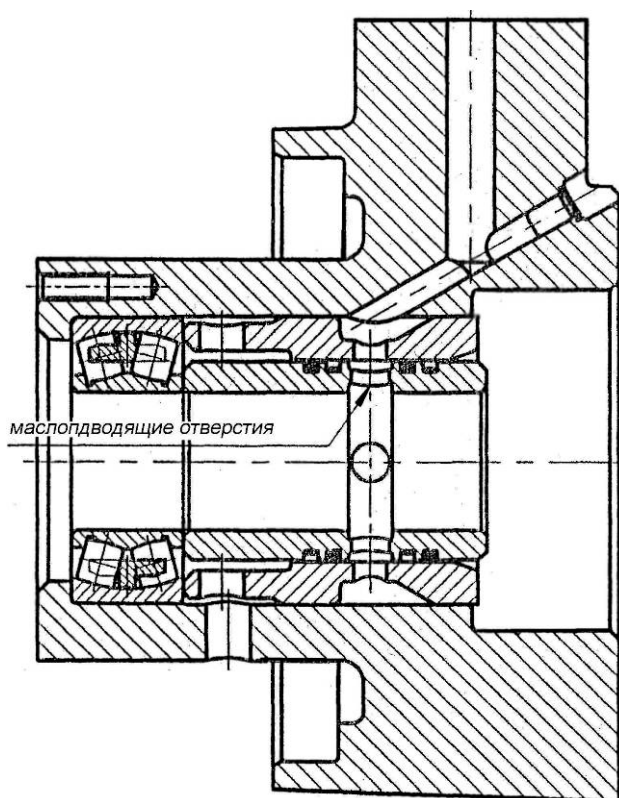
а – Установка распорных втулок в корпус привода вентилятора
